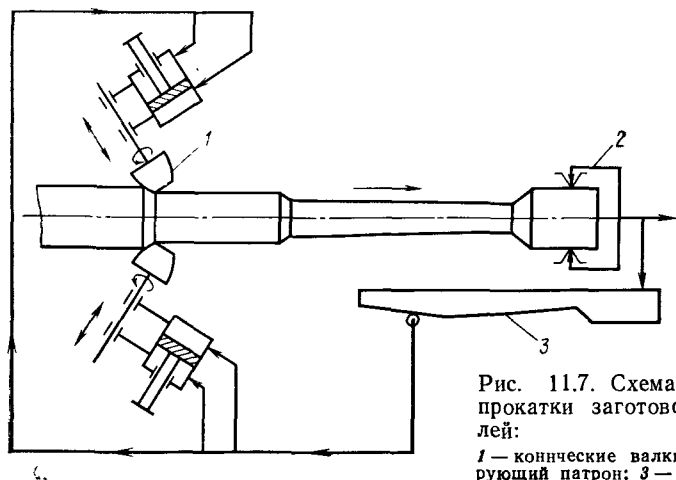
Схема периодической прокатки заготовок для шпинделей:
